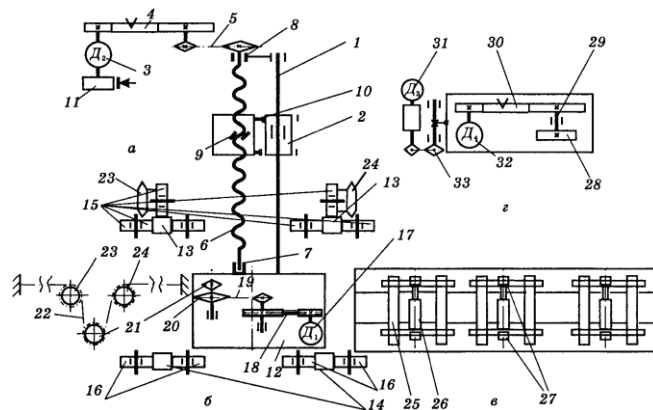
Кінематичні схеми механізмів горизонтального стрічкопилкового верстата: *a* – регулювання положення супорта; *б* – подачі; *в* – закріплення колоди; *г* – корування: 1 – стійка; 2 – гільза; 3, 17, 31, 32 – електродвигуни; 4, 18, 30 – пасова передача; 5, 19, 22, 33 – ланцюгові передачі; 6, 9 – гвинтова передача; 7, 8 – опора; 10 – тяга; 11 – гальмо; 12 – візок; 13, 14 – напрямні; 15, 16 – опори підшипникові; 20, 21, 23, 24 – зірочки ланцюгової передачі; 25 – затискач; 26 – гідроциліндр; 27 – пересувні упори; 28 – фреза; 29 – вал
